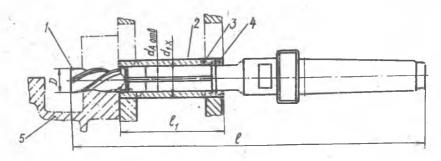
Схема обработки пазов фрезерованием: І — фреза; 2 — втулка; 3 — уплотнение; 4 — копир; 5 — профиль стыкового узла
